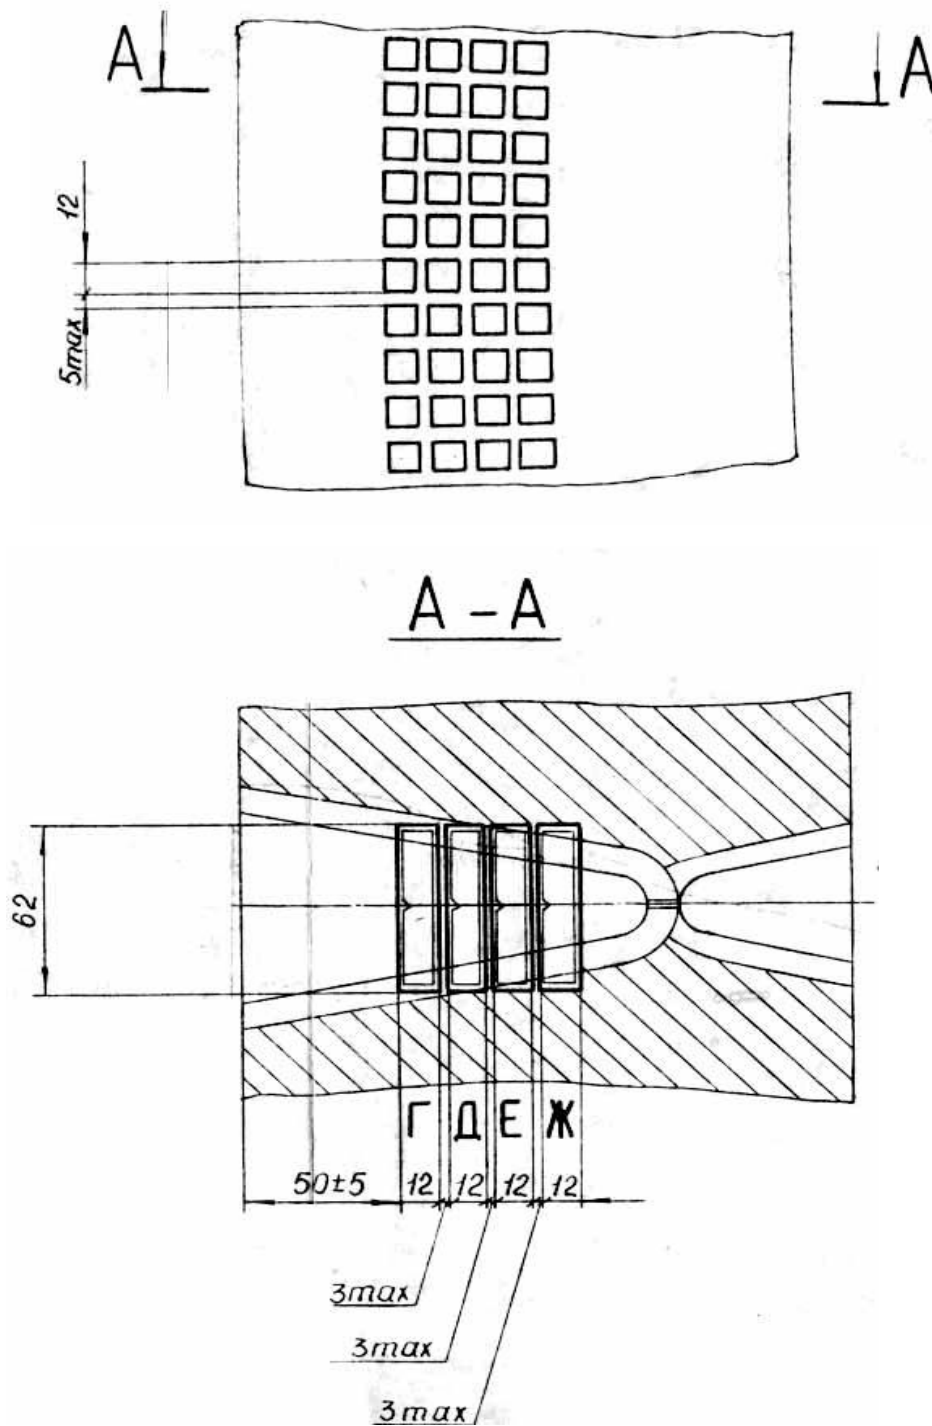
Схема вирізки зразків «Ш» із металу зварного шва
